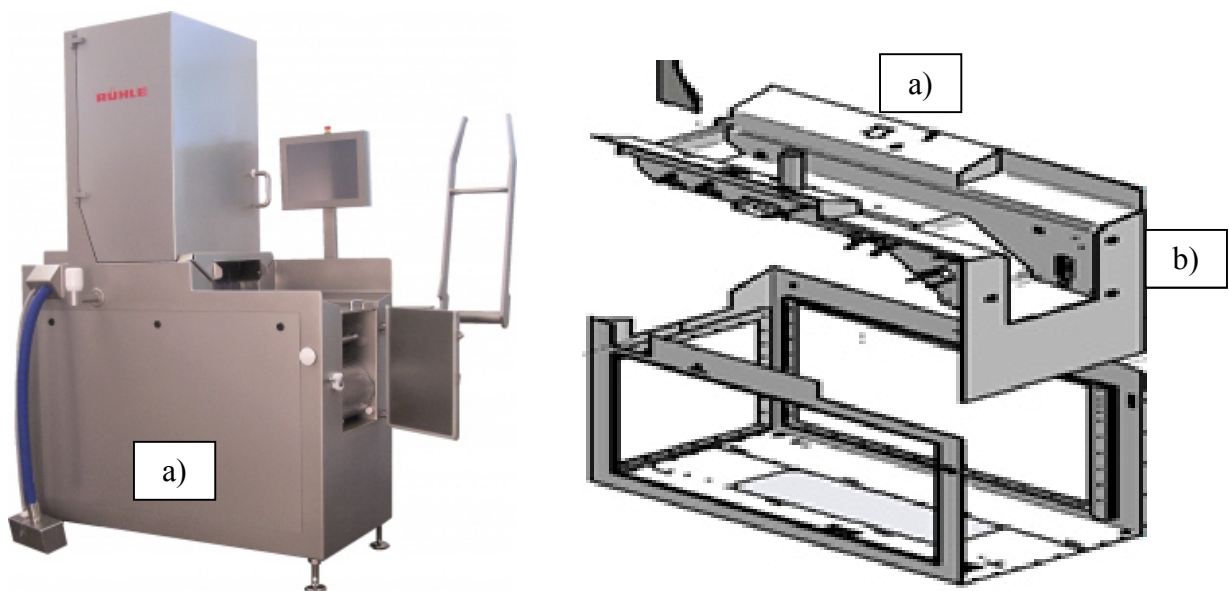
Machine injecteuse IR 56 : a) produit fini - b) phase de montage
